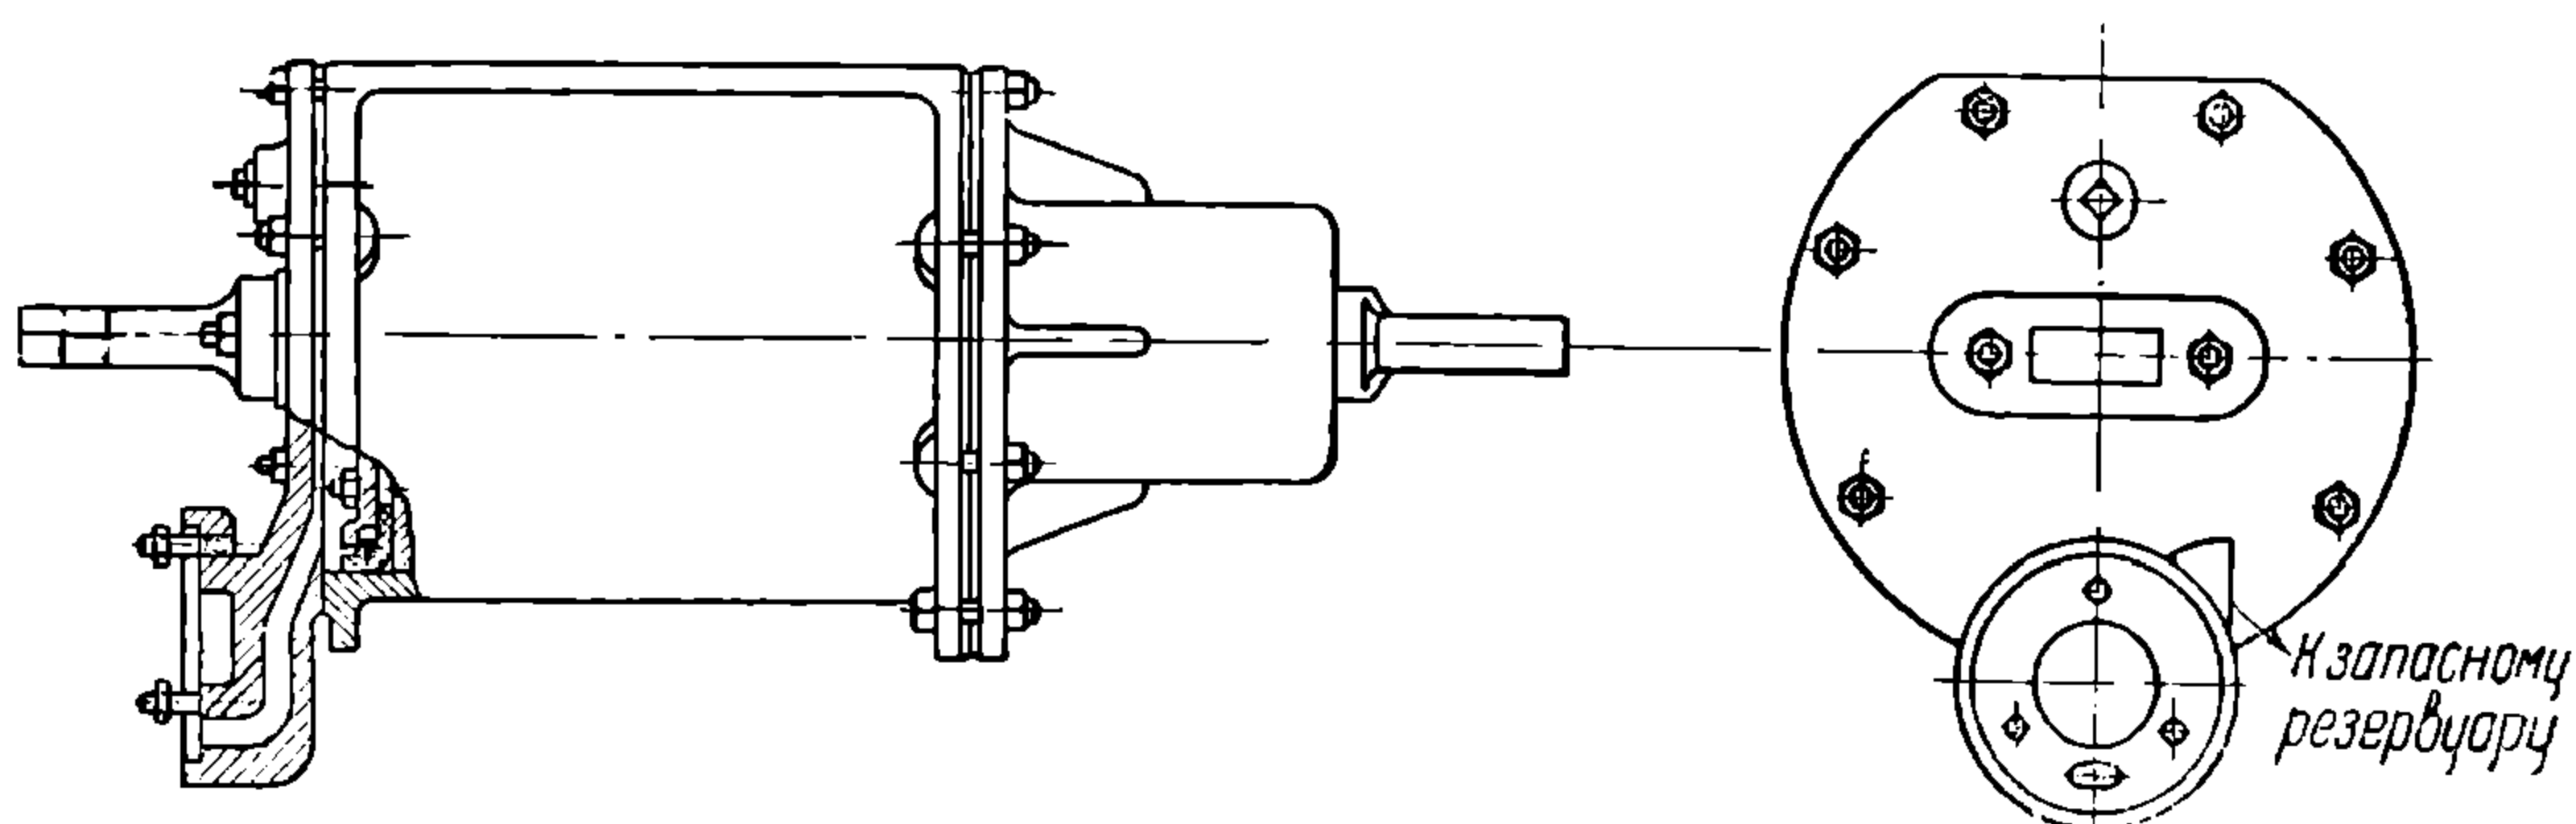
Приспособление марки «Рояль» в разрезе.
